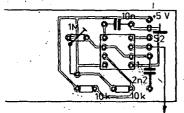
Obrazec plošných spojů desky T123 (strana spojů)
